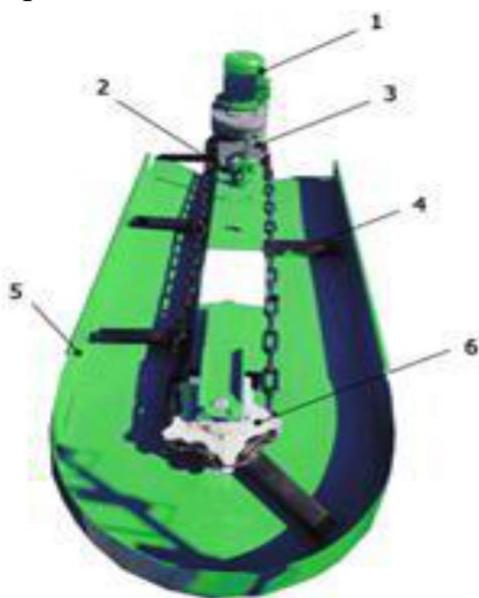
Автоматичний натяжний пристрій конвеєра КСГ-7:
